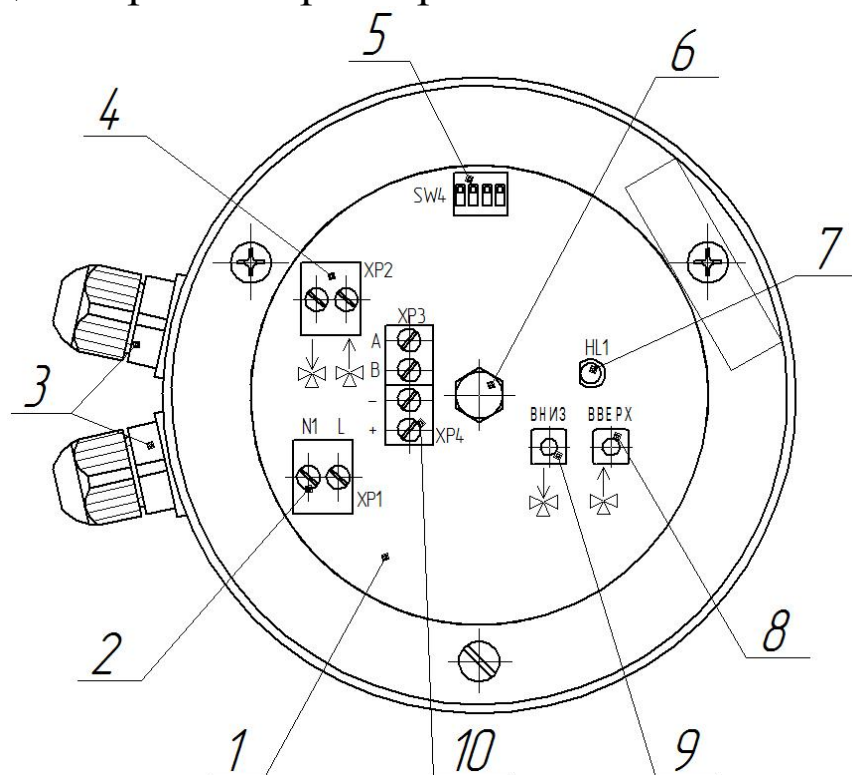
Привод ЭП-100 и ЭП-180 с открытой крышкой
